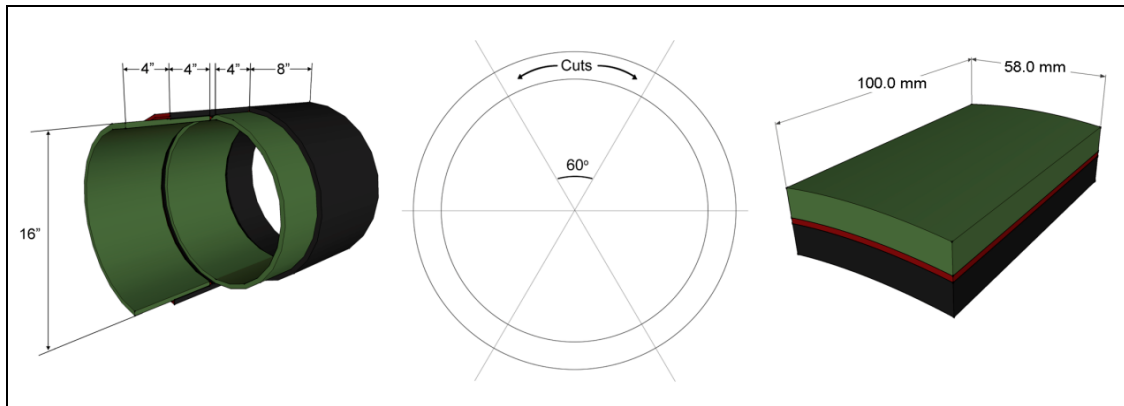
Dimensões e cortes dos tubos de 16 polegadas.
